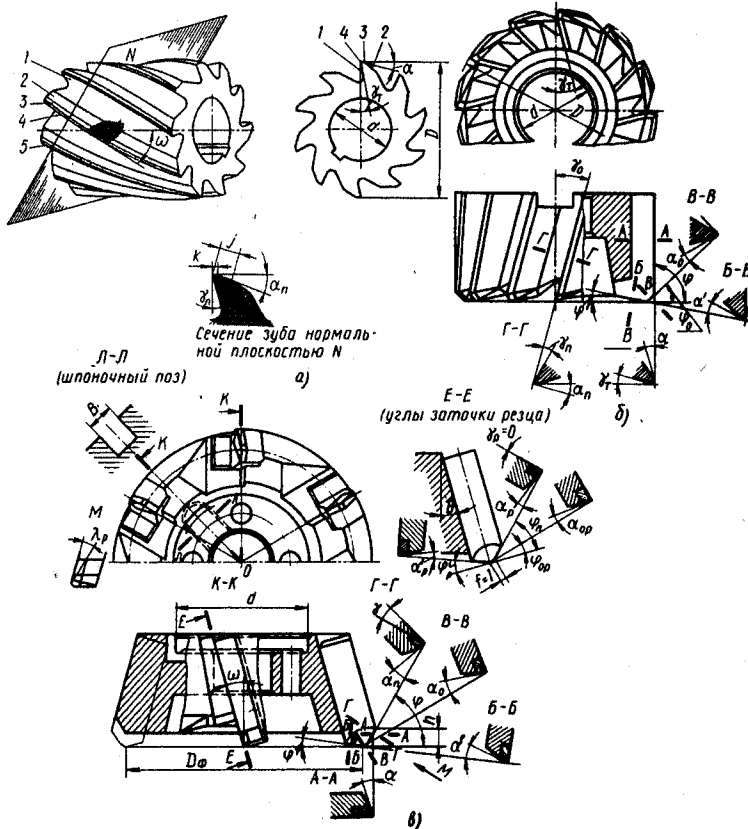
Геометрические параметры цилиндрической фрезы (а), торцовой насадной фрезы (б) и торцовой фрезерной головки (в)
